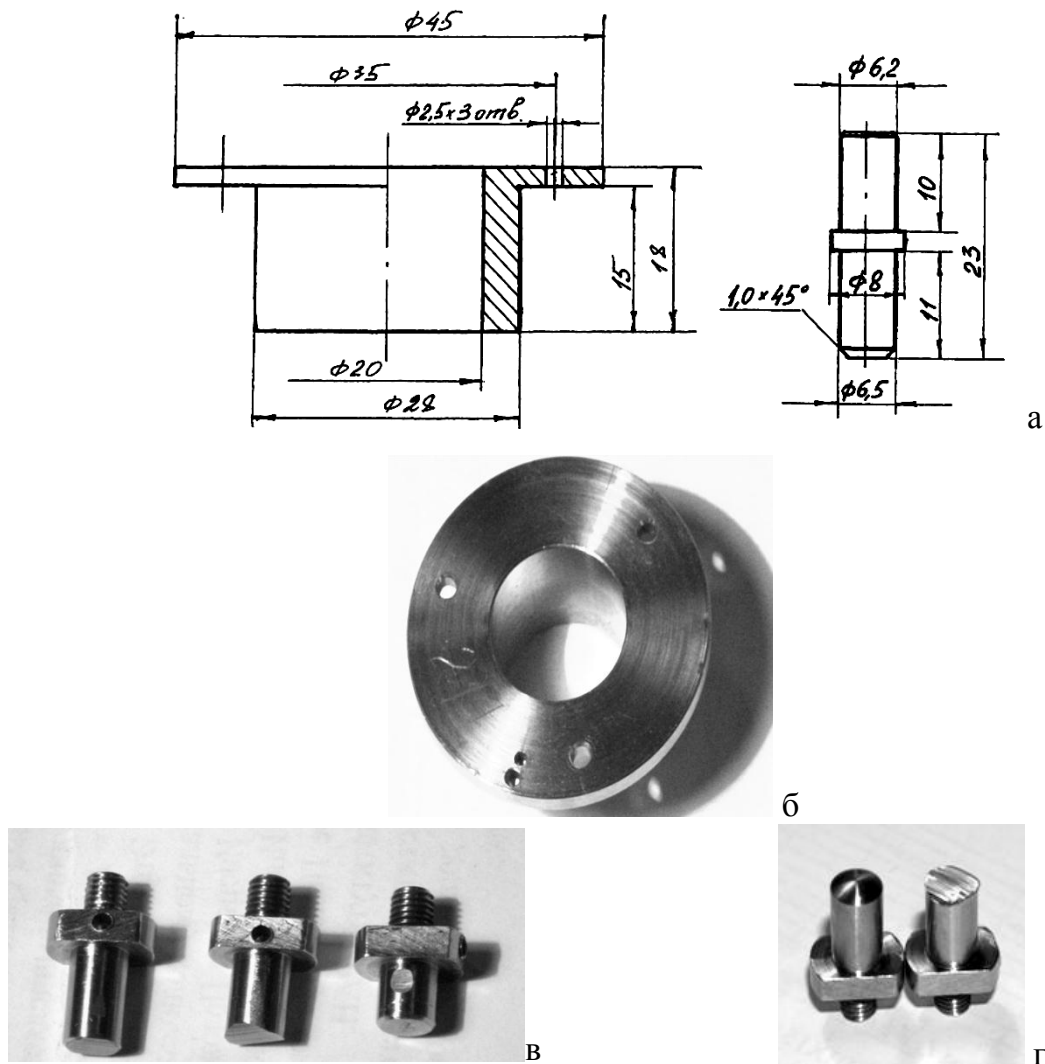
Образцы для испытаний: а - чертежи пальчикового и кольцевого образцов, б - фотография кольцевого образца, в, г - фотографии пальчиковых образцов до и после испытаний
